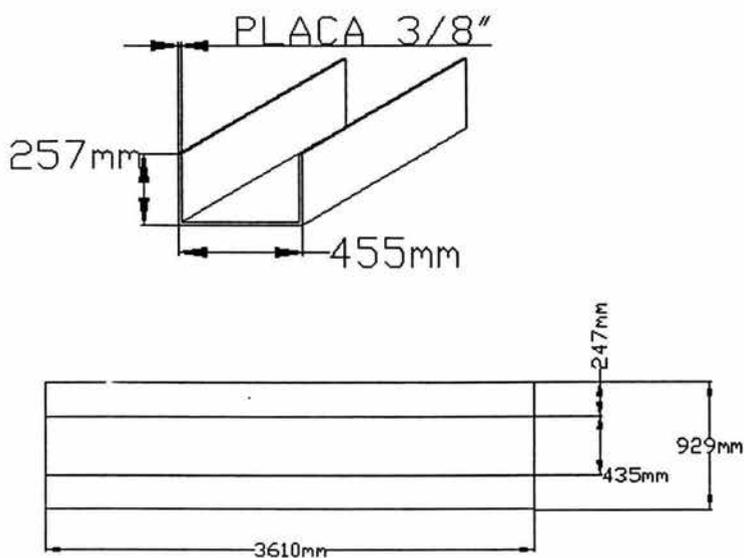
Ejemplo del dimensionamiento de la placa de sector sin sujeción para su corte y doblado.
